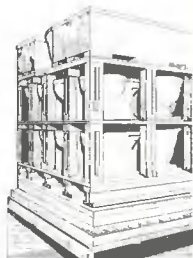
Карборундовая этажерка для загрузки вагонеток санитарными фарфоровыми изделиями
